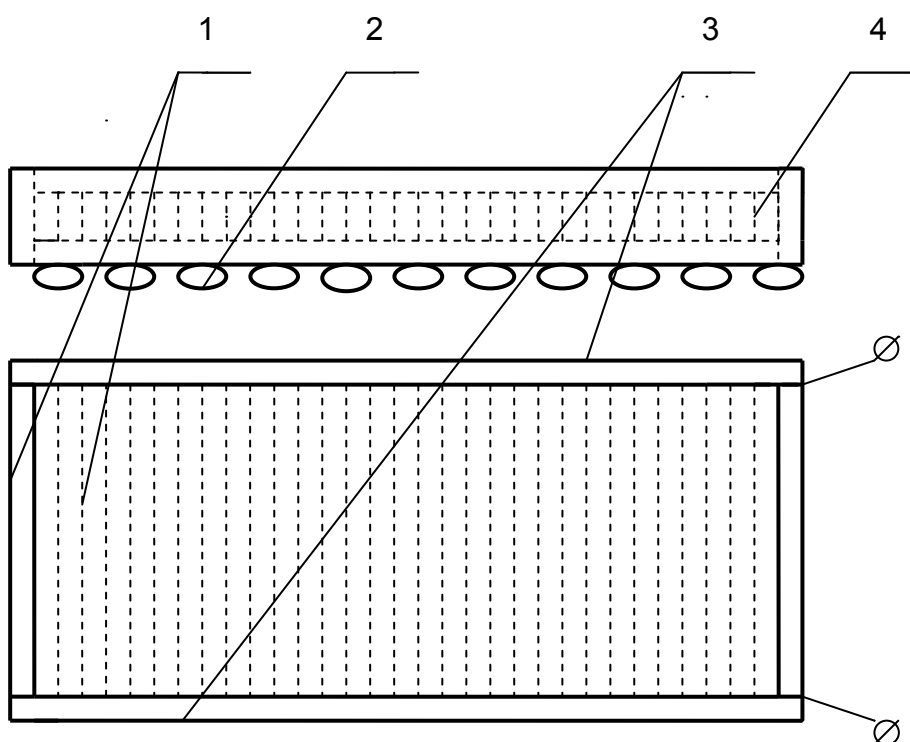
Конструкция преобразователя «Гибкий пакет»
